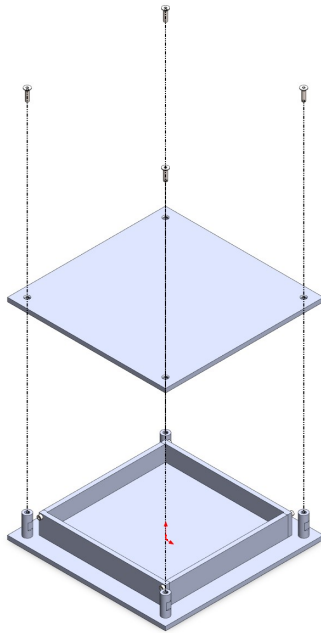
Vista explodida do molde e da tampa e respectivas linhas de montagem
